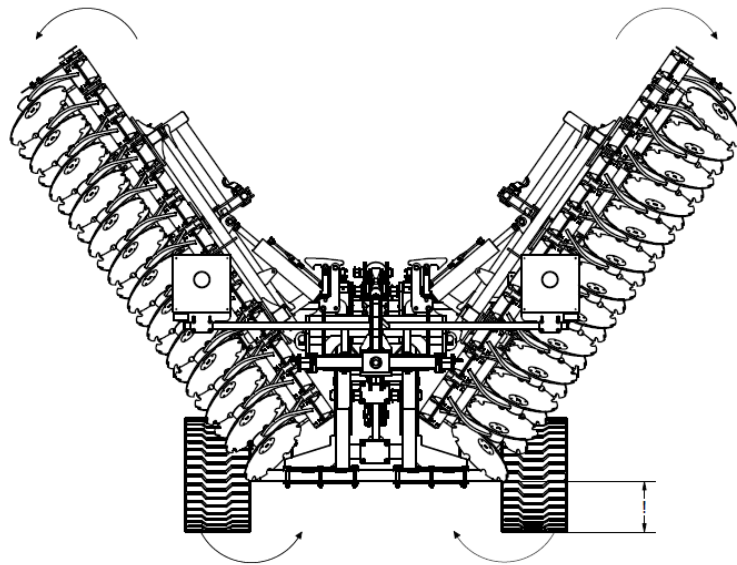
Étapes du dépliage de la machine : la machine s'ouvre, les extrémités des bras latéraux sont à une hauteur convenable.
